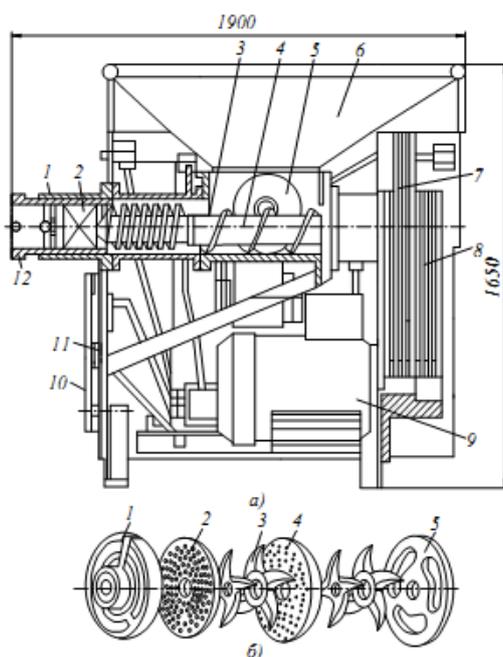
Волчок К7-ФВП-160-2: а – схема волчка; б – режущий механизм
